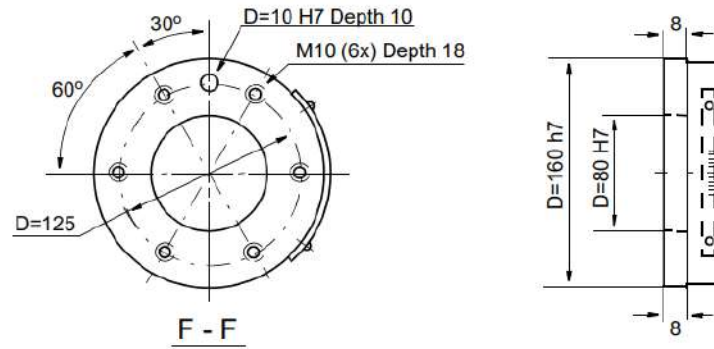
Dimensiones de la brida de montaje del robot en mm. [16]
